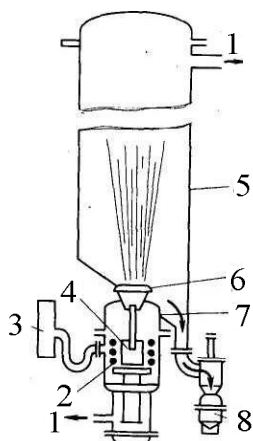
Схема установки для вакуумного розпорошення розплавлених металів: 1 — відвід до вакуумному насоса; 2 — індуктор; 3 — генератор для живлення індуктора; 4 — тигель з розплавом алюмінію; 5 — камера розпорошення; 6 — затвор; 7 — камера плавлення; 8 — контейнер для порошку
